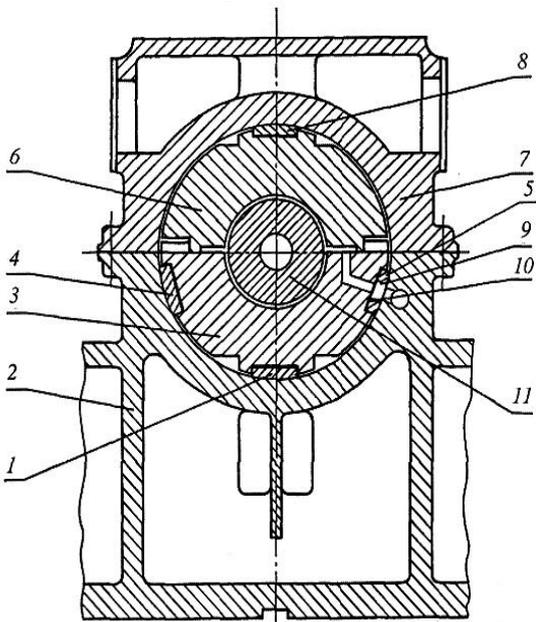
Установка вкладыша опорного подшипника в корпусе
